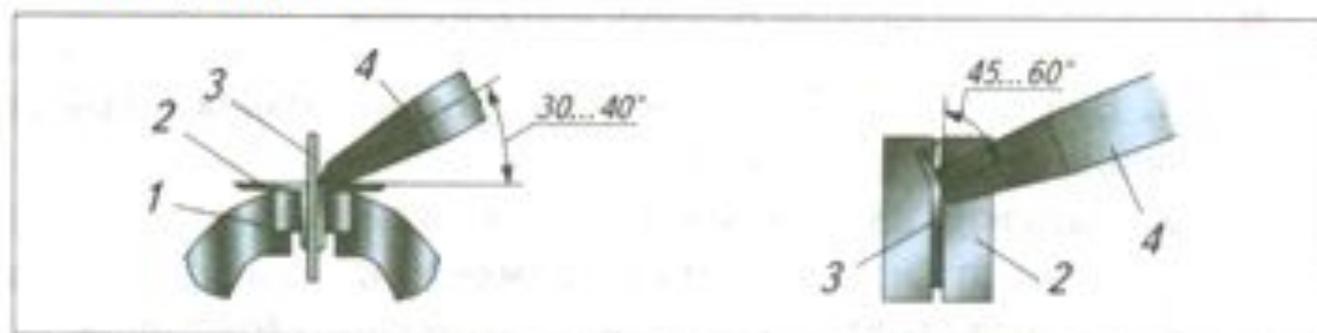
Положение зубила при рубке в тисках: 1 — тиски; 2 — нагубники; 3 — заготовка; 4 — зубило
